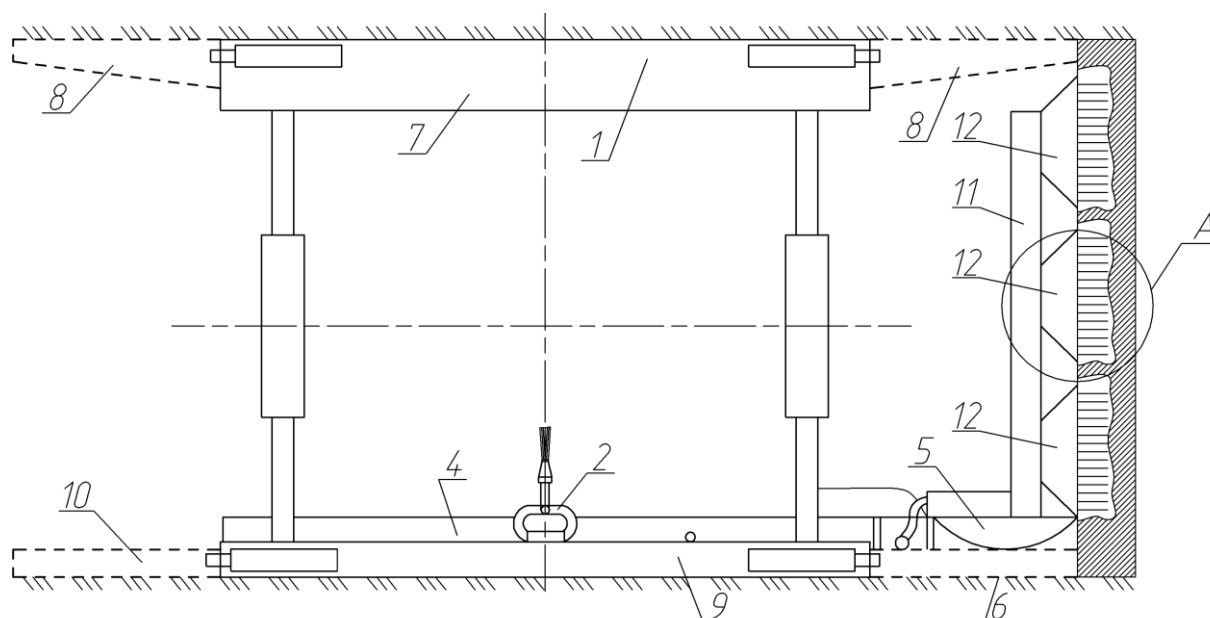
Проходческо-очистной гидравлический механизированный комплекс (вид с торца)
